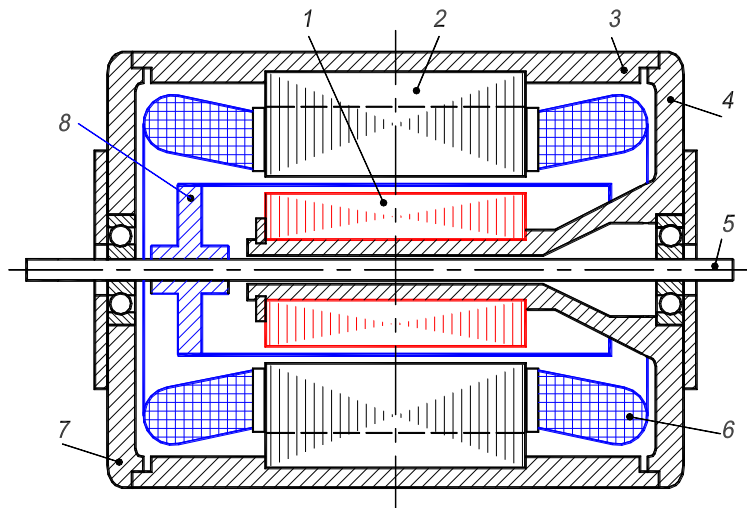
Конструктивная схема исполнительного асинхронного двигателя с полым ротором: 1 – внутренний неподвижный сердечник статора; 2 – внешний неподвижный сердечник статора; 3 – корпус статора; 4, 7 – подшипниковые щиты; 5 – вал; 6 – обмотка статора; 8 – вращающийся полый ротор
